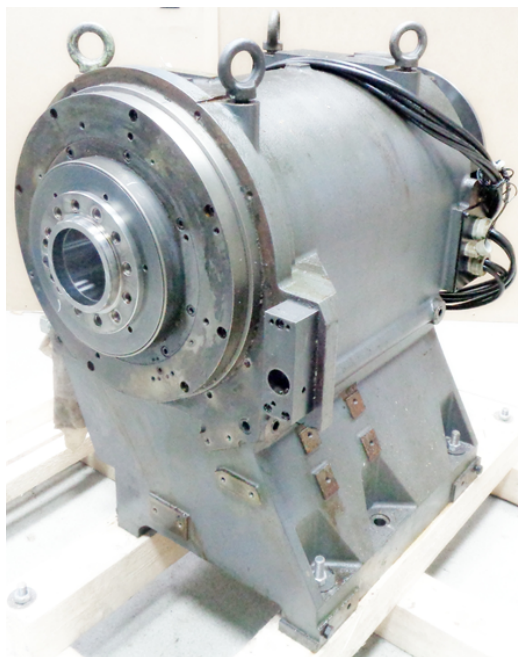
Общий вид ШУ токарного многоцелевого станка Mori Seiki NL3000
